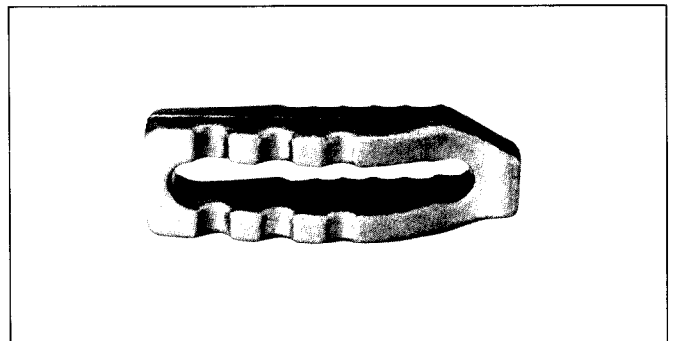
Gesenkschmiedete Spannpratze (0,7 kg) aus C 35 zur Aufspannung von Werkzeugen für Kunststoff-Spritzgießmaschinen
